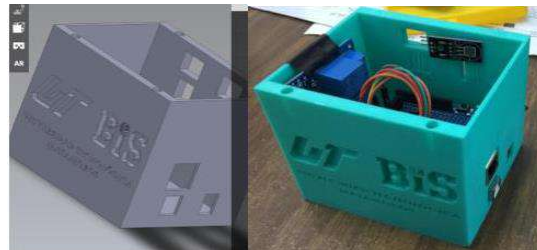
visualización de diseño modelado en 3D de carcasa y posteriormente si impresión en 3D
